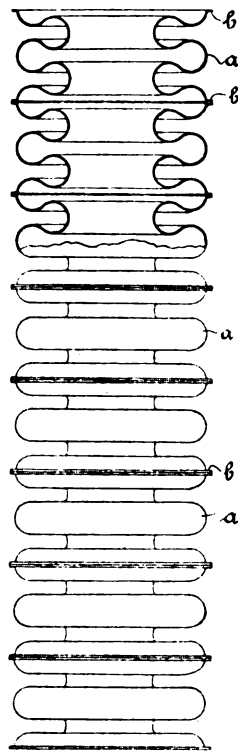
Geschweißter Schlauch aus mehrweiligen Rohrstücken.
